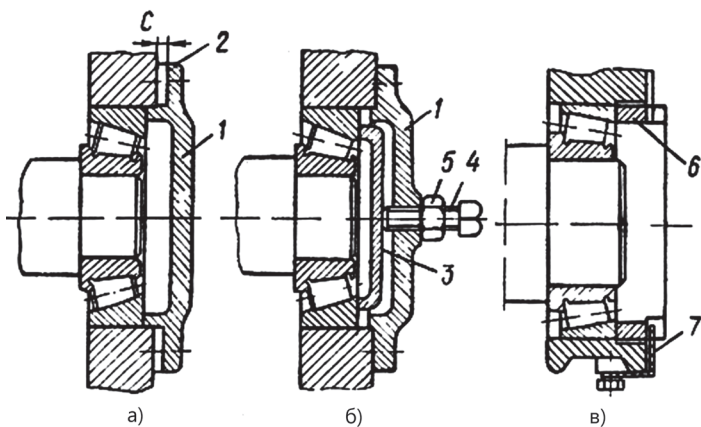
Схемы регулирования зазора в конических роликоподшипниках:
